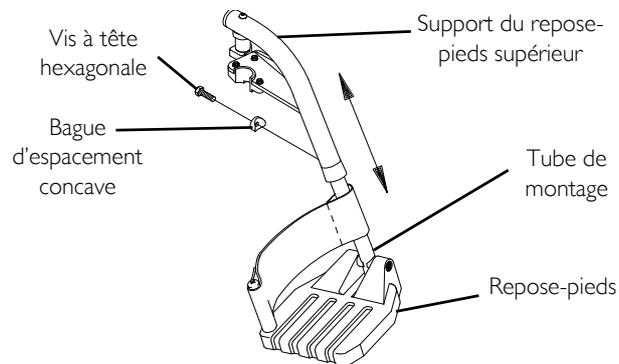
FIGURE I Réglage de la hauteur des repose-pieds - 60°, 70° et 70° à fuseau
